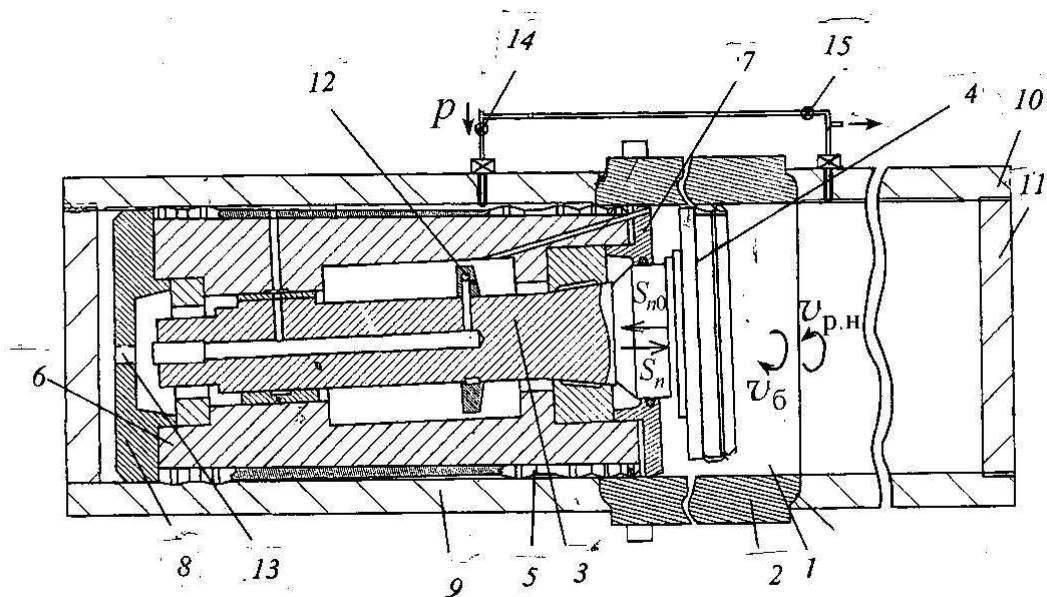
Режуще-деформирующее малогабаритное устройство для обработки глубоких отверстий в трубных заготовках вихрефрезерованием по методу винтовой интерполяции
